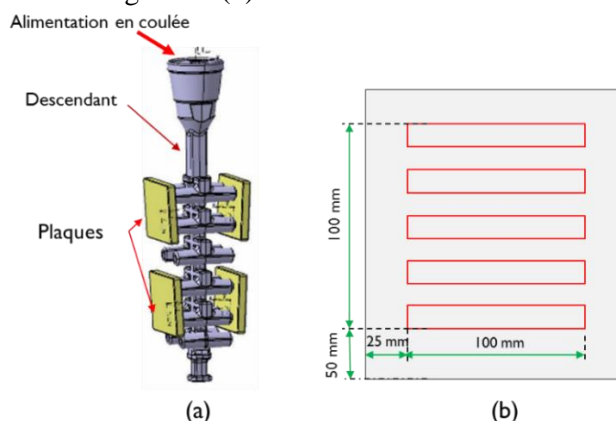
a) Grappe de coulée des plaques PMP permettant la coulée de 4 plaques simultanément, b) dimensions de plaque ainsi que positions de prélèvement d'éprouvettes.
